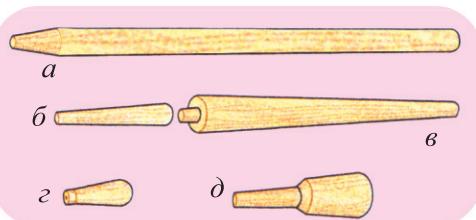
Детали цилиндрической и конической формы: а – черенок для лопаты; б – ручка для киянки; в – ножка стула; г – ручка для напильников и стамесок; д – картофелемялка
